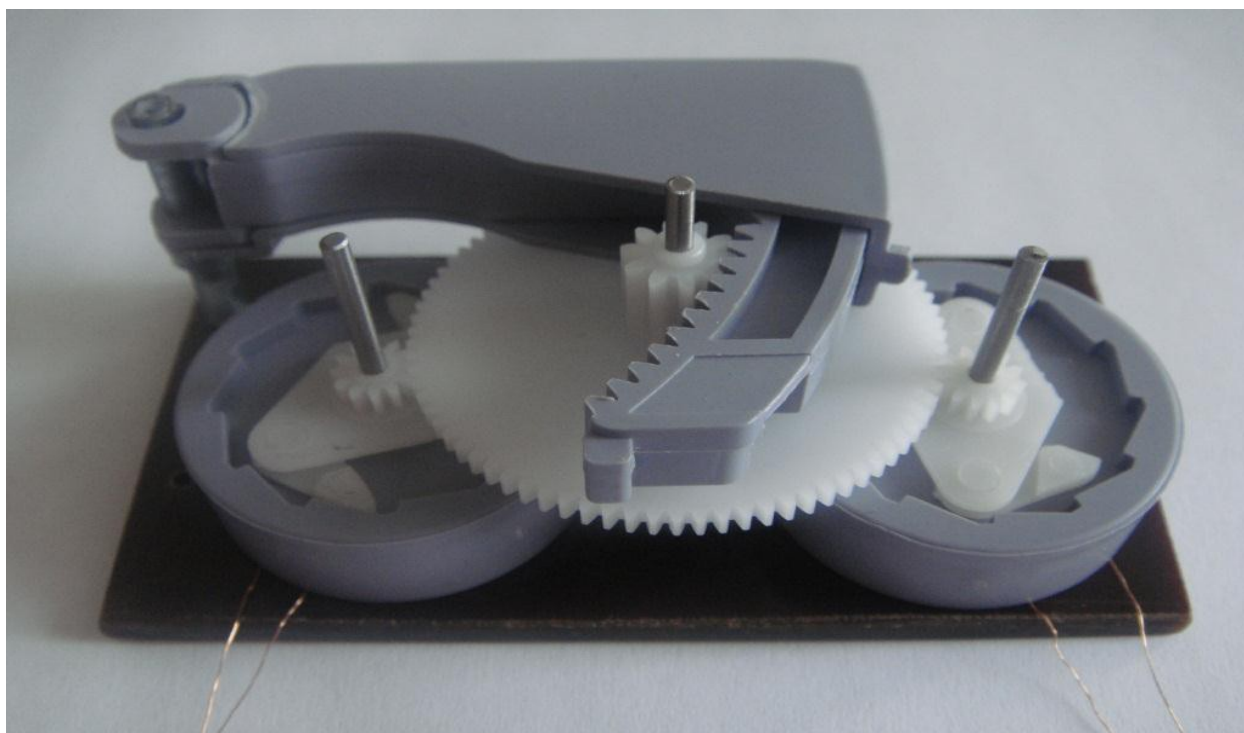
Механизм, соединяющий зубчатый рычаг с генератором
